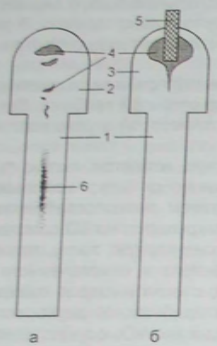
Схемы расположения усадочных раковин и усадочной рыхлоты в цилиндрических отливках
